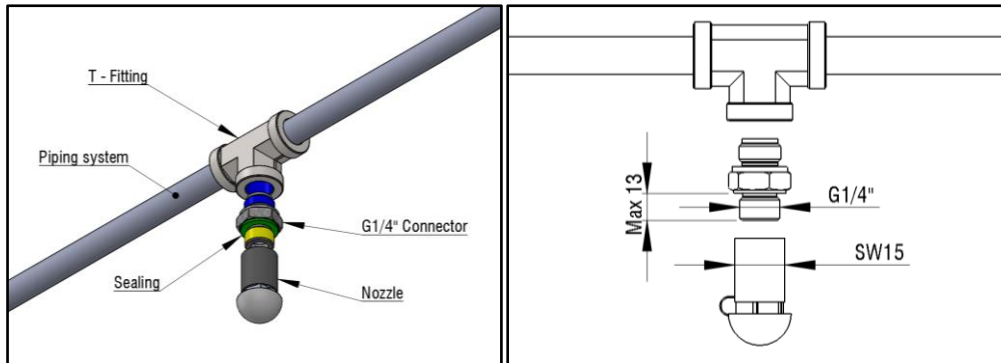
Montaje de los difusores mediante accesorios de tubería roscados
